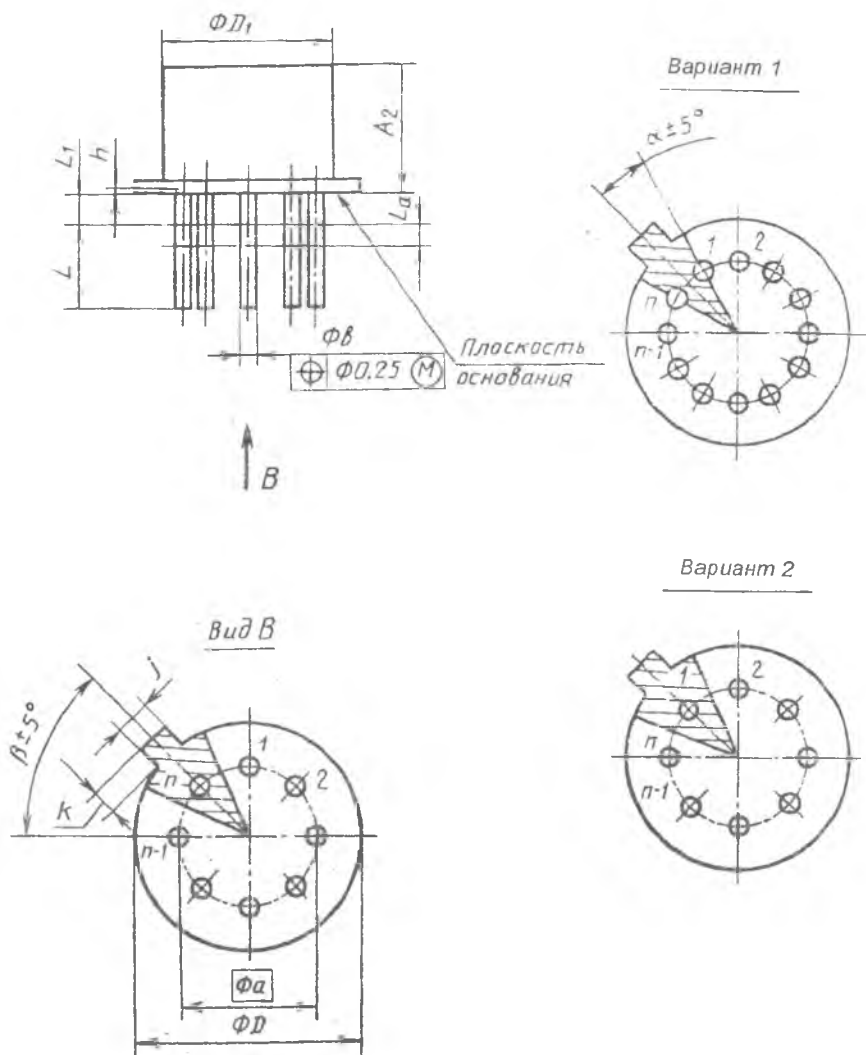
Конструкция корпуса типа 3 подтипа 1
